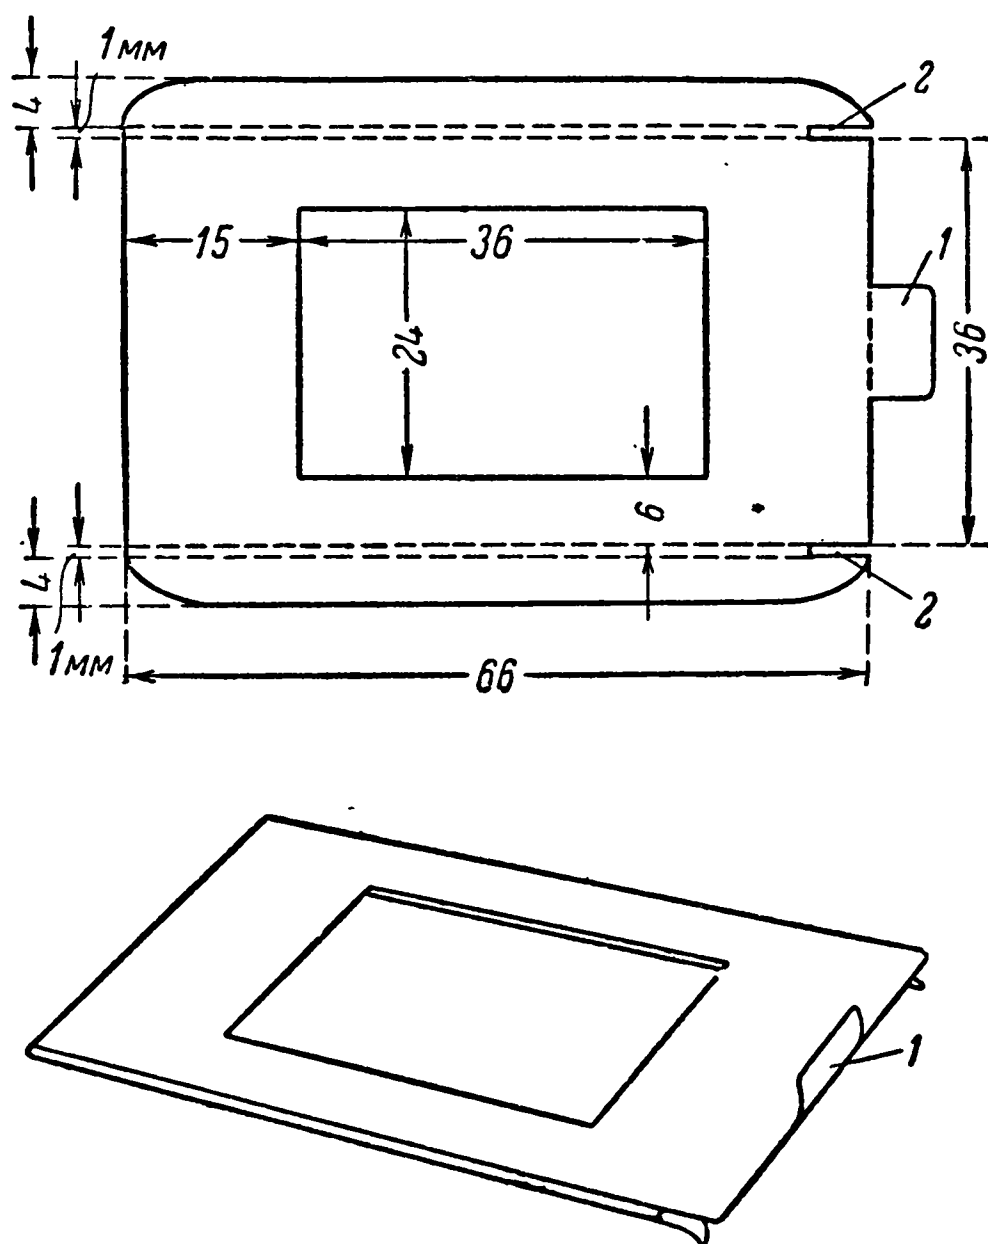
Негативная рамка: вверху—развертка, внизу—рамка в готовом виде
